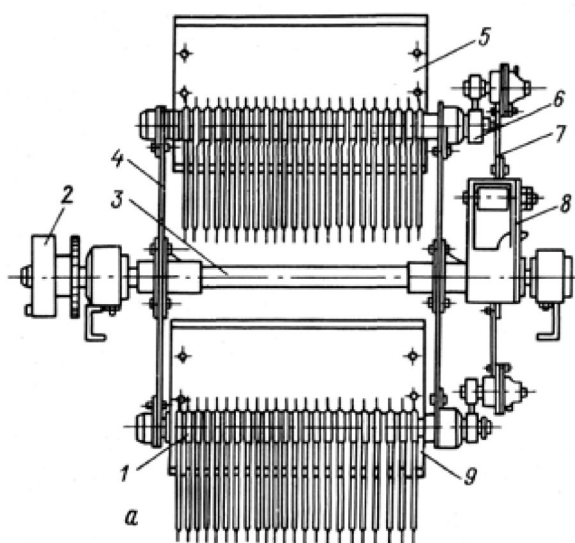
Очесывающий барабан: 1 – гребень; 2 – муфта свободного хода; 3 – вал; 4 – диск барабана; 5, 9 – вертикальная и горизонтальная лопасти; 6 – кривошип; 7 – направляющий диск; 8 – эксцентрик
